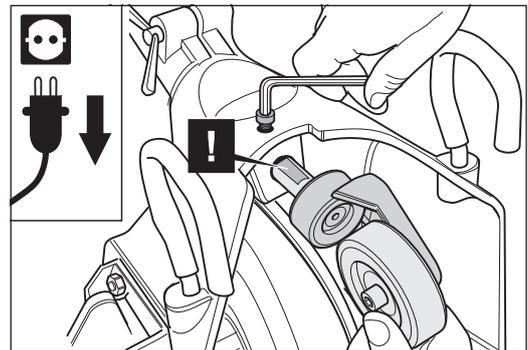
Die Klemmschraube lösen und das komplette Hinterrad aus dem Maschinengehäuse ziehen. Beim Einbau die Spannfläche der Spornachse zur Schraube hin ausrichten.
